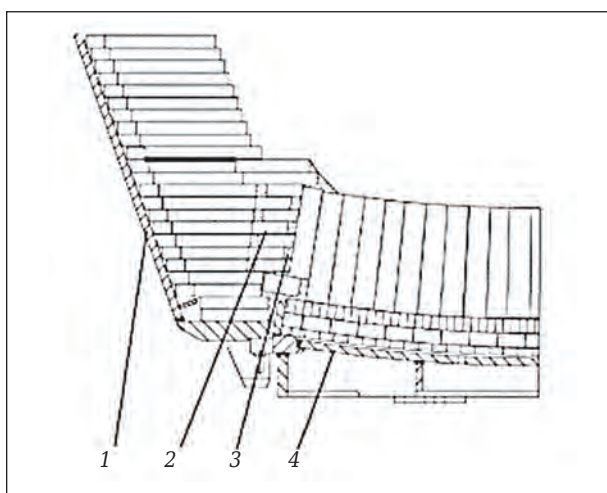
Новая конструкция стыка футеровки конвертера с отъемным днищем: 1 — изделия для арматурного слоя стен; 2 — новый дополнительный формат кирпича; 3 — набивная масса; 4 — отъемное днище
